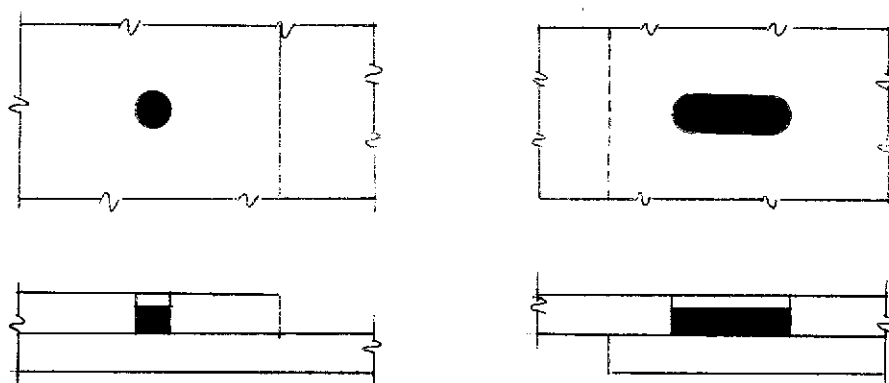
Soldaduras de tapón y de ranura.
